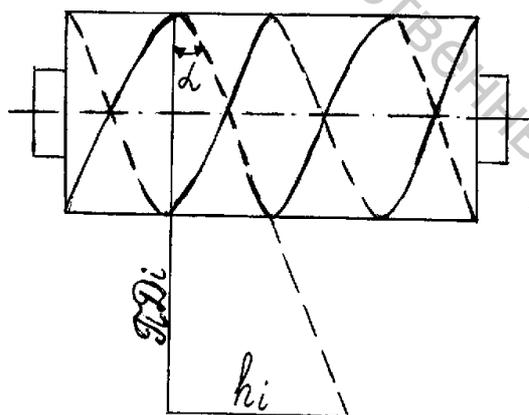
Развертка цилиндрической поверхности намотки бобины
